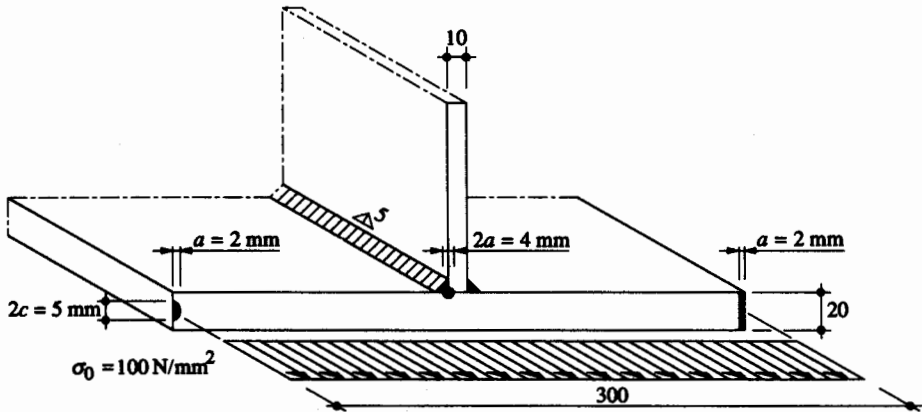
Fissures dans la section d'une poutre composée à âme pleine (les dimensions des fissures ne sont pas à l'échelle !).
